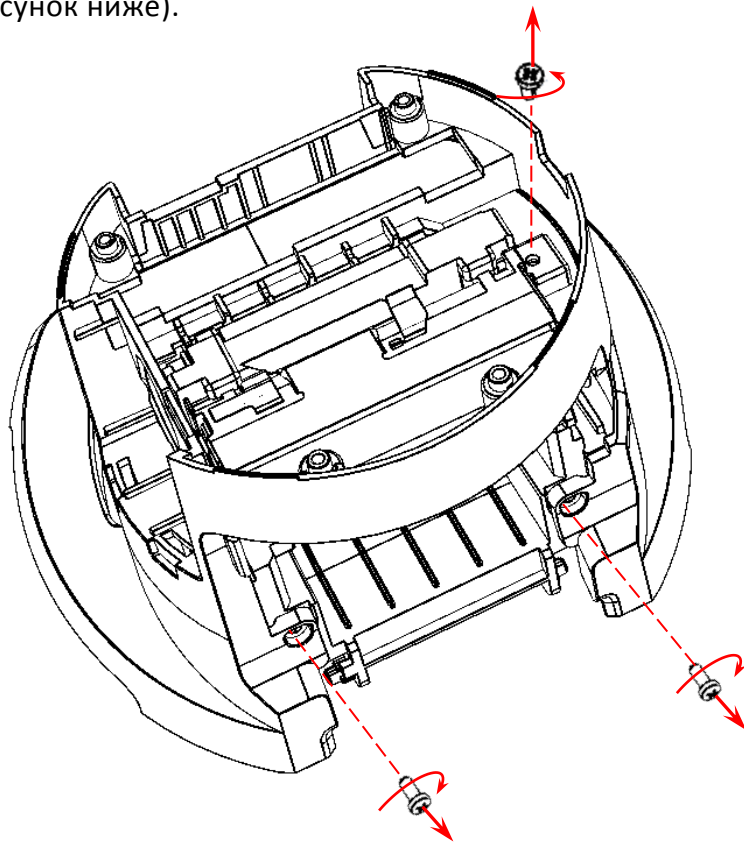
Винты крепления лотка для ЧЛ к стойке (расположенные с внешней стороны)
